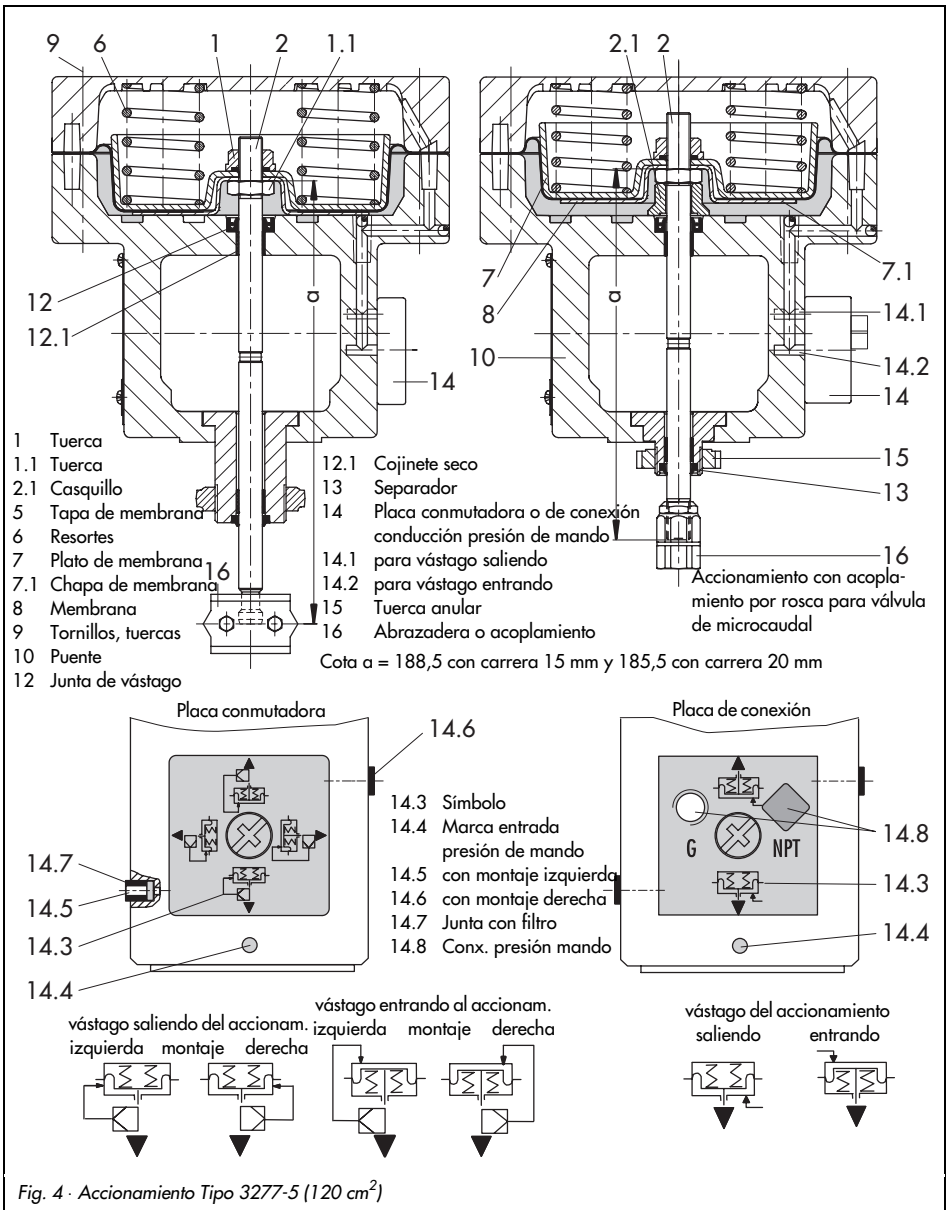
· Accionamiento Tipo 3277-5 (120 cm²)
